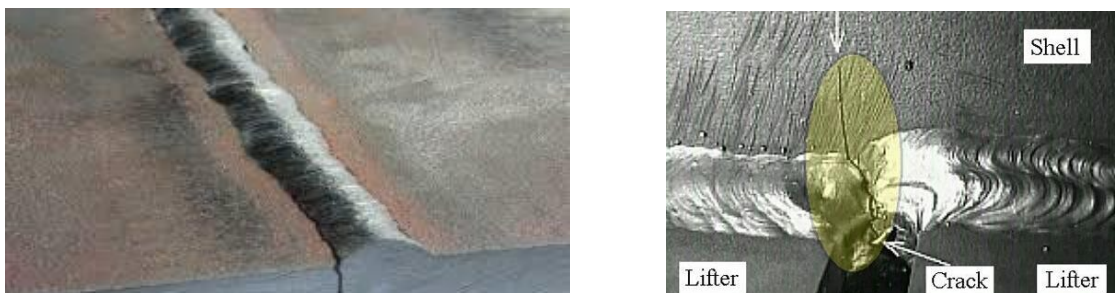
Примеры возникающих при сварке и наплавке горячих трещин
